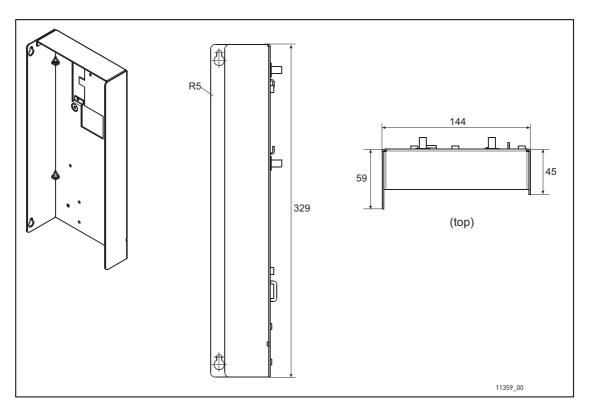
Dimensiones de la caja de montaje de la unidad de control
